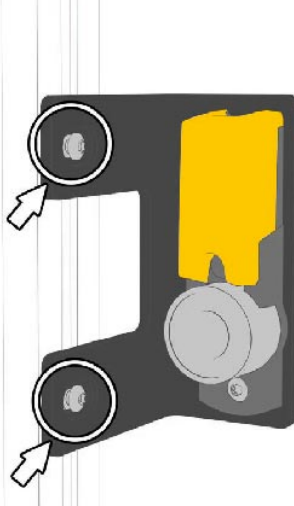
Montageplatte mit Prozesszuhaltung am Profil anbringen und und Schrauben M8 x 12 mm Torx festziehen.
